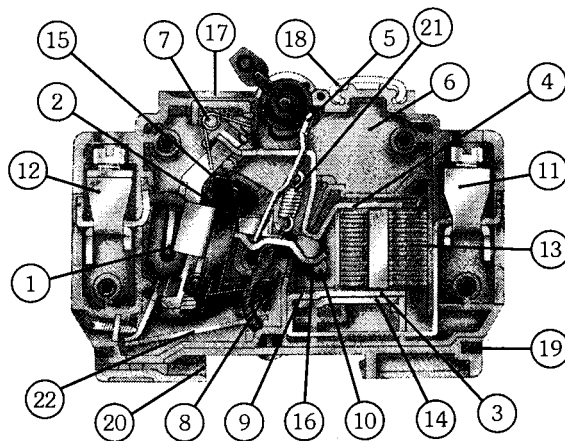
Vista interna e componentes do disjuntor termomagnético UNIC. Cortesia: Pial-Legrand.
